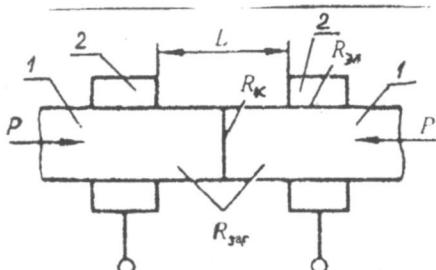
Схема контактной сварки: 1 – заготовки;
